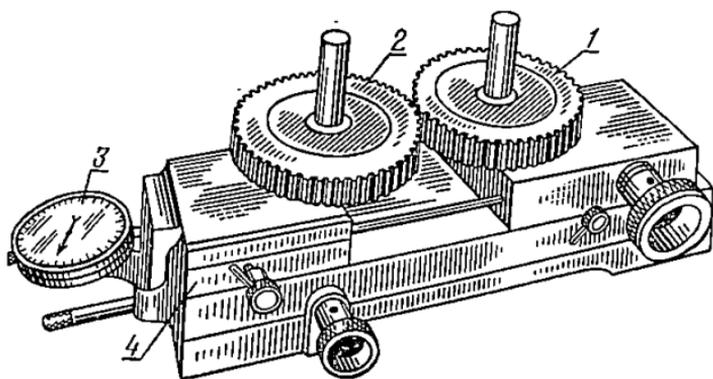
Контрольное приспособление для проверки зубчатых колес:
